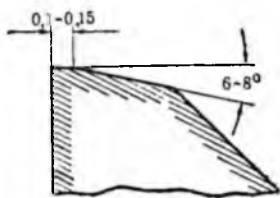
Угол заточки затылка режущей кромки зубцов фрез и разверток.
